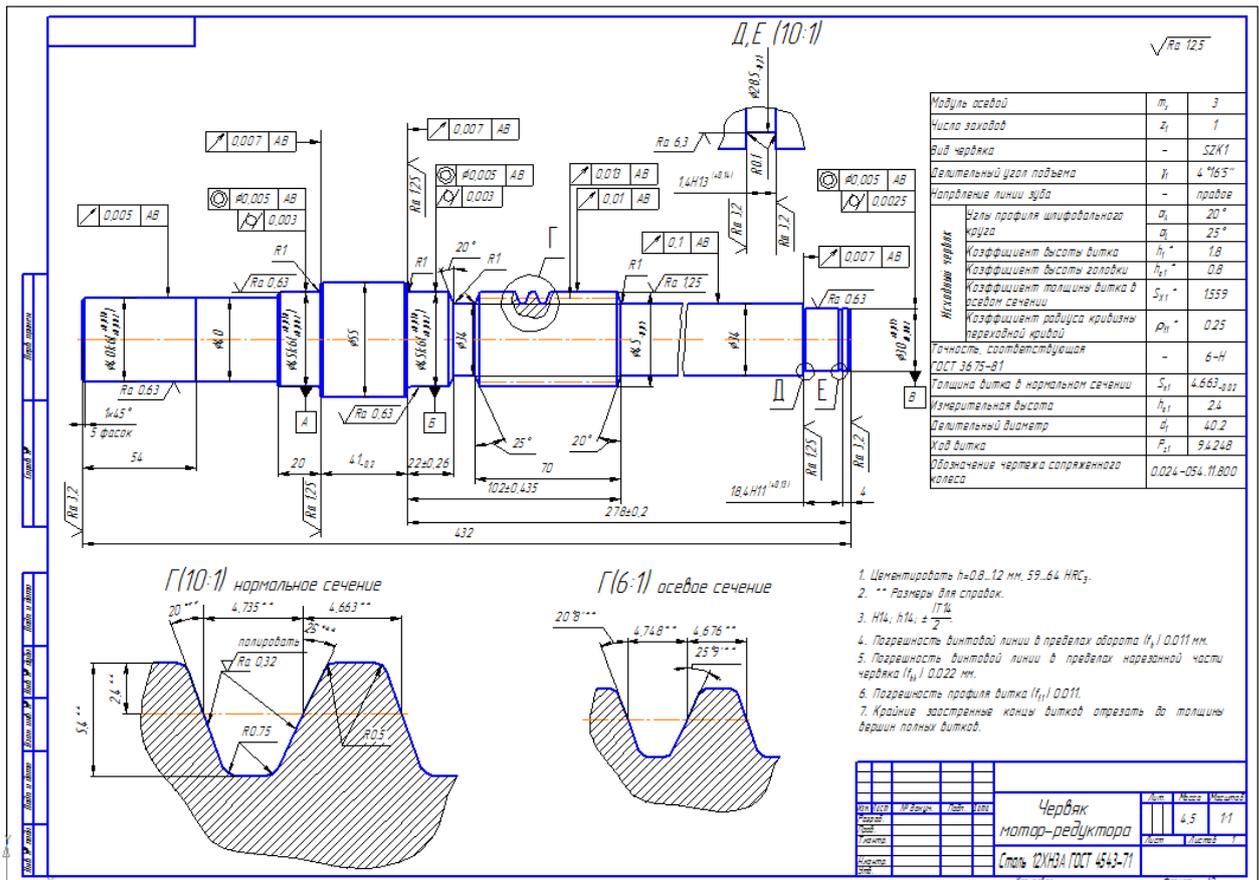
Рабочий чертеж червяка мотор-редуктора
